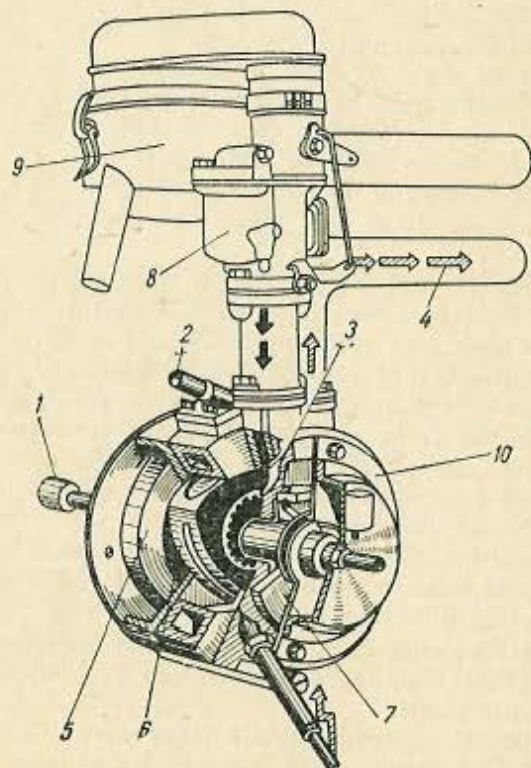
Motorul cu piston rotativ NSU-Wankel.
